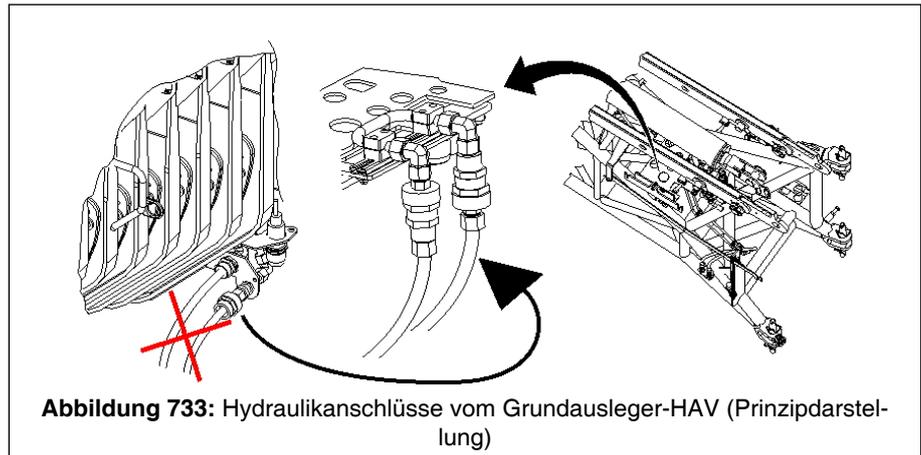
Hydraulikanschlüsse vom Grundausleger-HAV (Prinzipdarstellung)
